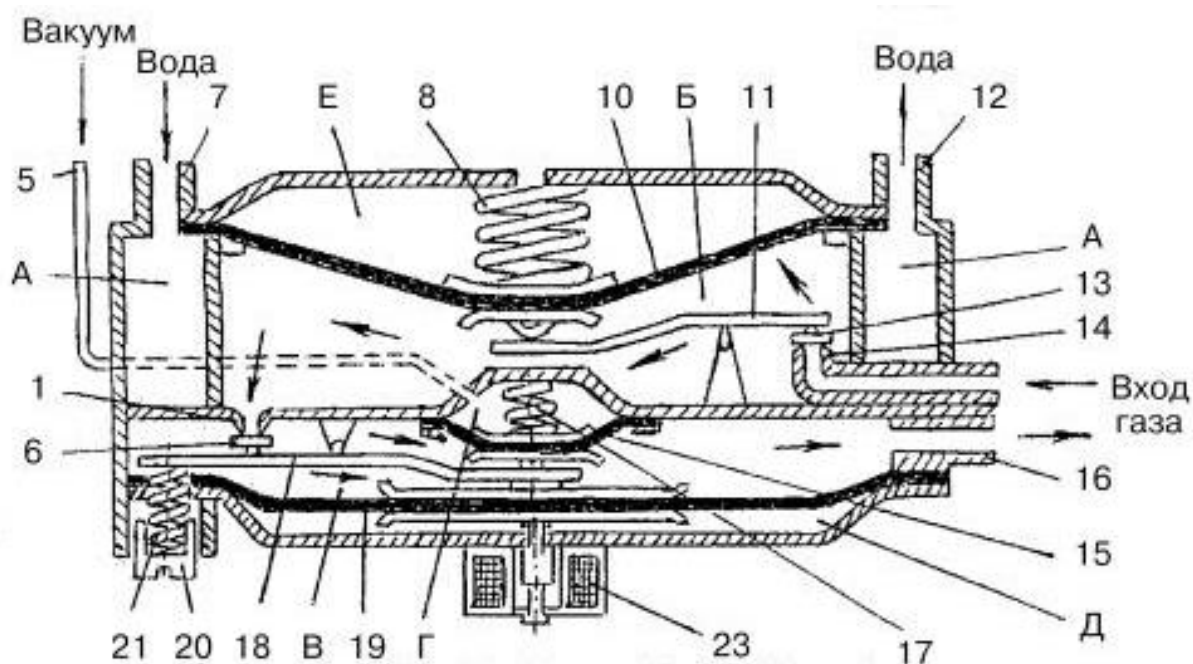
Двухступенчатый газовый редуктор – испаритель.
